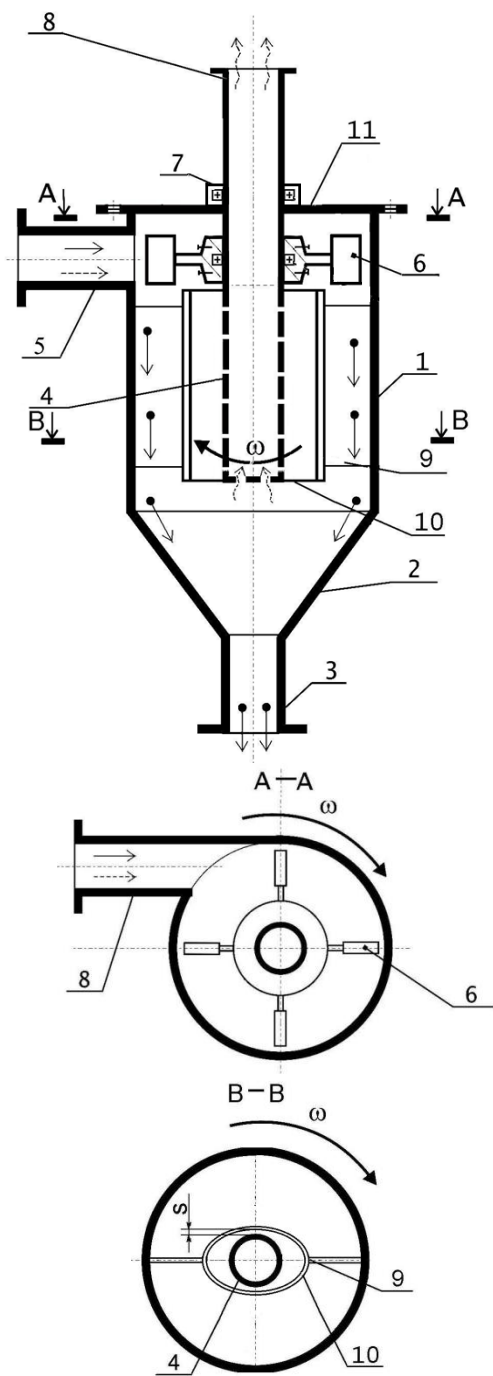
Фильтр-циклон: 1 – цилиндрический корпус; 2 – коническое днище; 3 – штуцер удаления уловленной пыли; 4 – фильтровальный элемент; 5 – тангенциальный патрубок; 6 – лопасти; 7 – подшипниково-уплотнительное устройство; 8 – выходной патрубок; 9 – крепление обечайки; 10 – эллиптическая обечайка
